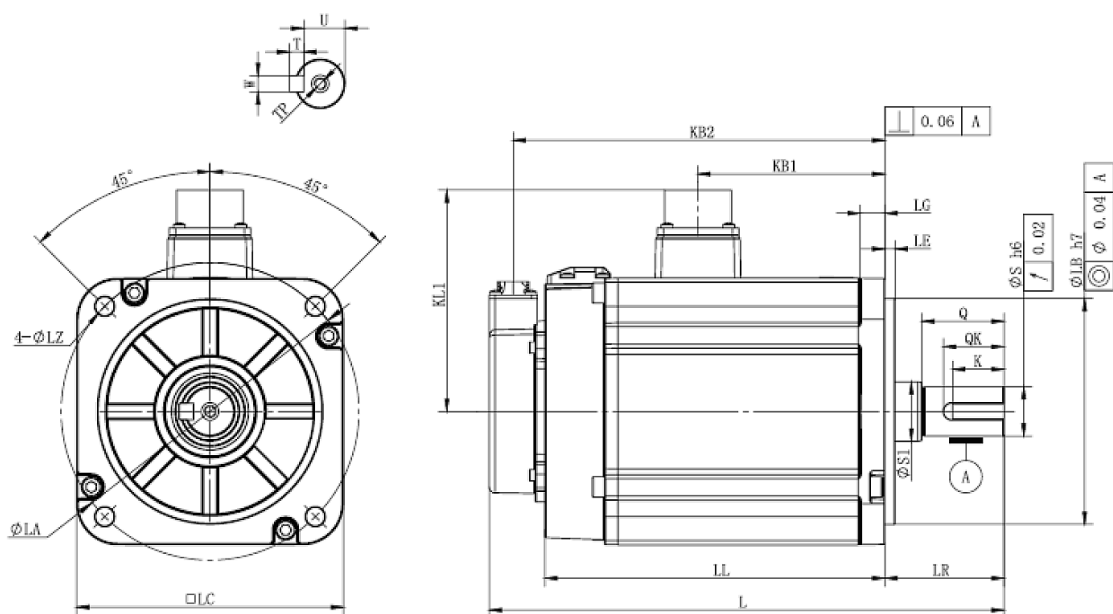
Габаритные и установочные размеры двигателей с фланцем 60 мм
